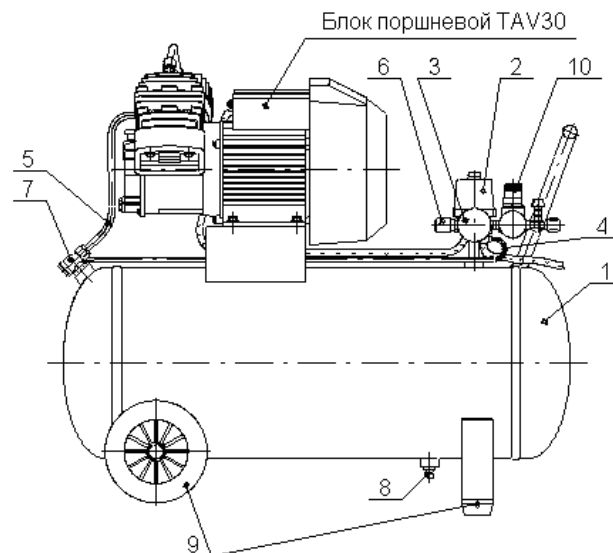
Общий вид компрессора СБ4/С-50.Ј2047В
